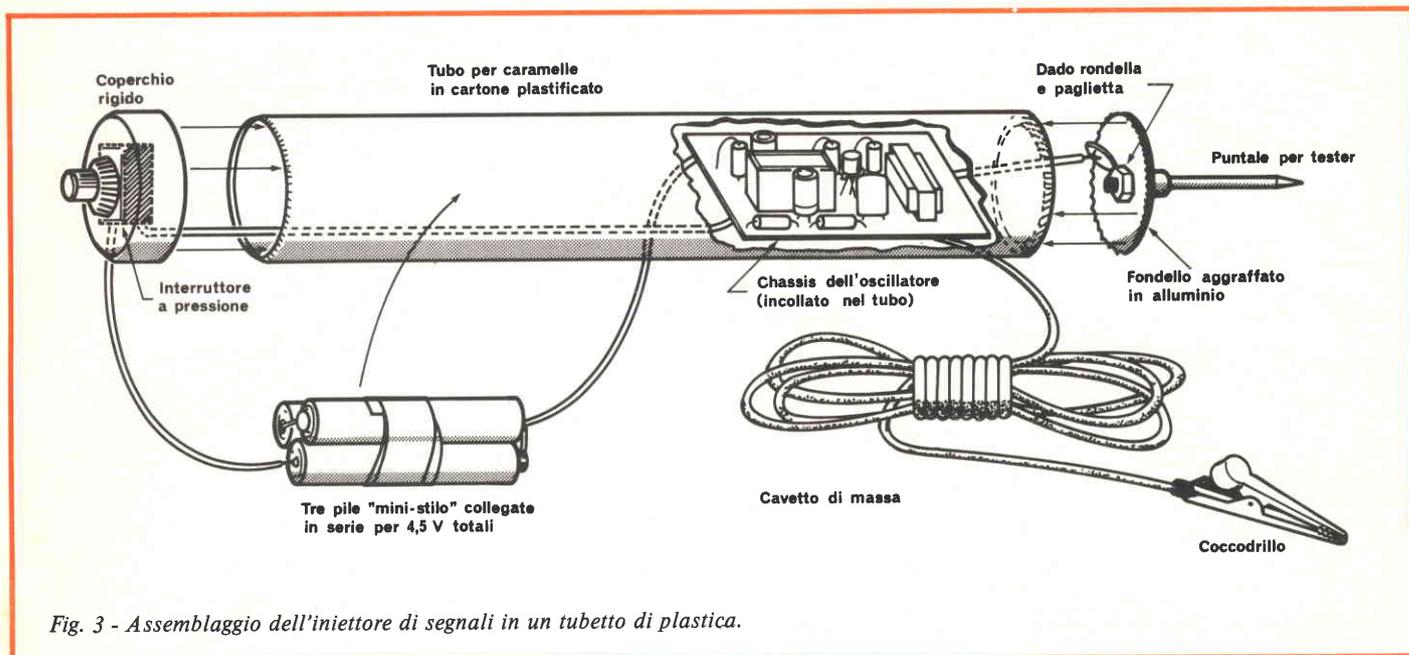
Assemblaggio dell'iniettore di segnali in un tubetto di plastica.
